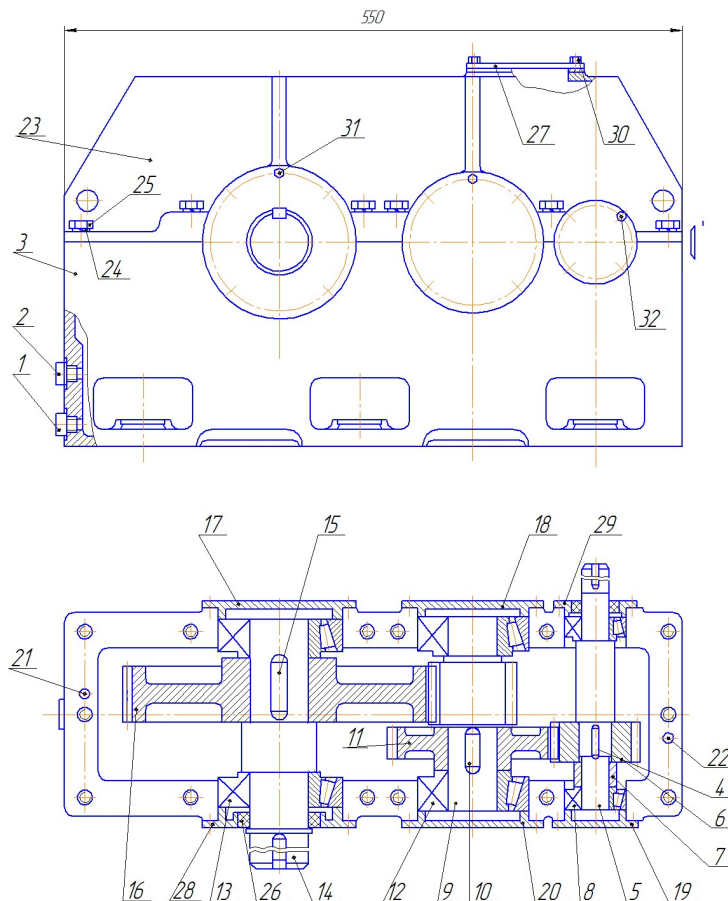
Редуктор двоступінчастий циліндричний Ц2У-400Н
